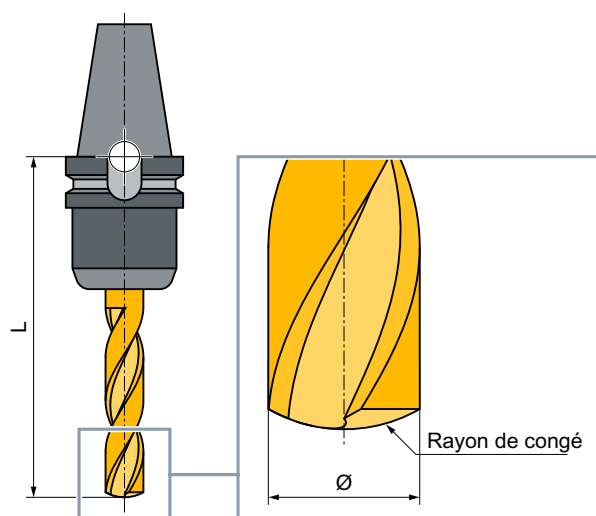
Exemple d'outil 3D : fraise à bout rond (type 111)
